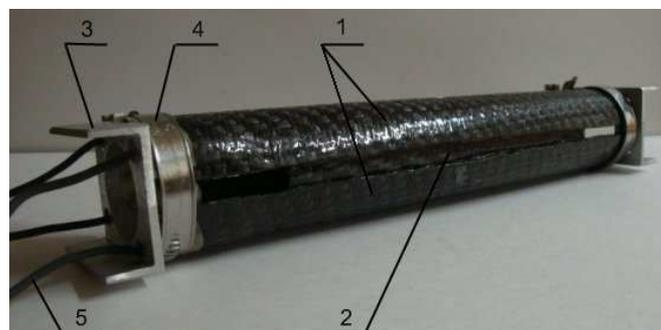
Конструкция шарнира в сборе: полуцилиндрические элементы — 1, цилиндрический элемент — 2, переходники из алюминиевого сплава АМГ6 — 3, хомут — 4, провода для соединения нагревателей с источником тока — 5
